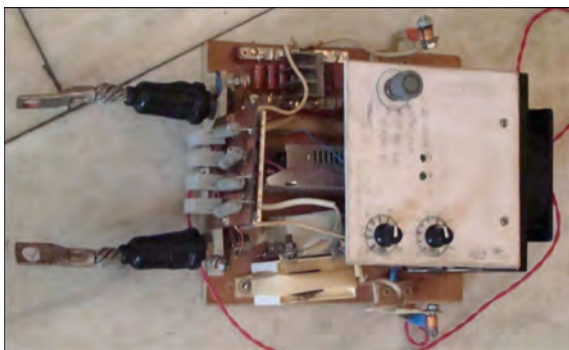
Пристрій-приставка для тандемного ММА зварювання
